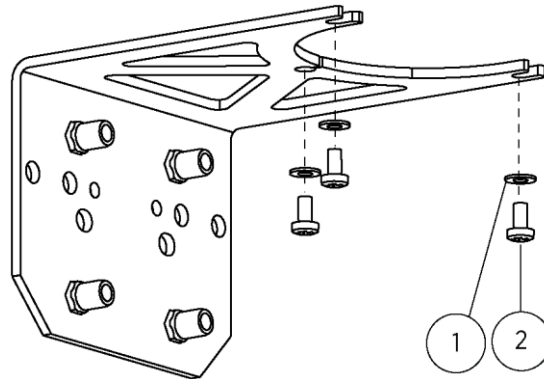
Схема монтажного кронштейну для установки приладу AQТ420:
